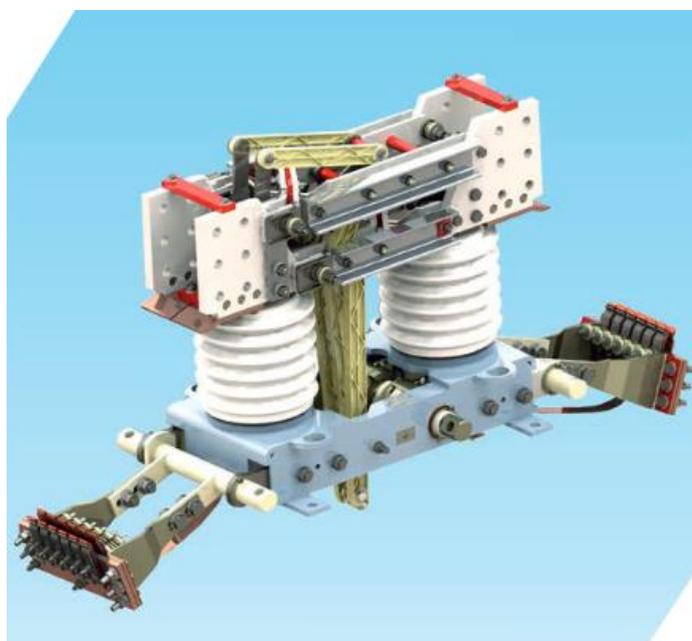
Общий вид разъединителя РРТЗ-20/8000УХЛЗ
